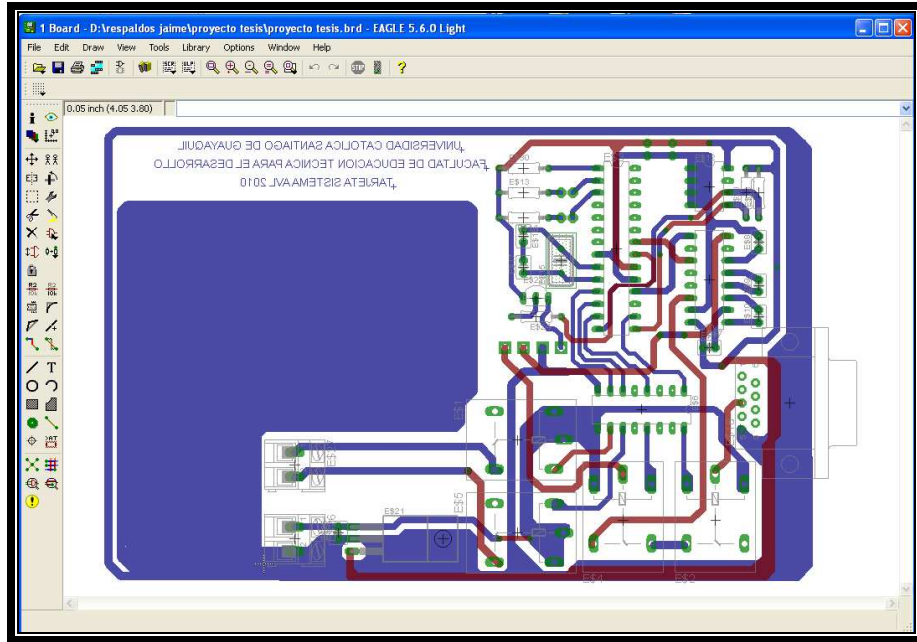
Diseño de la tarjeta impresa TECNICA1
